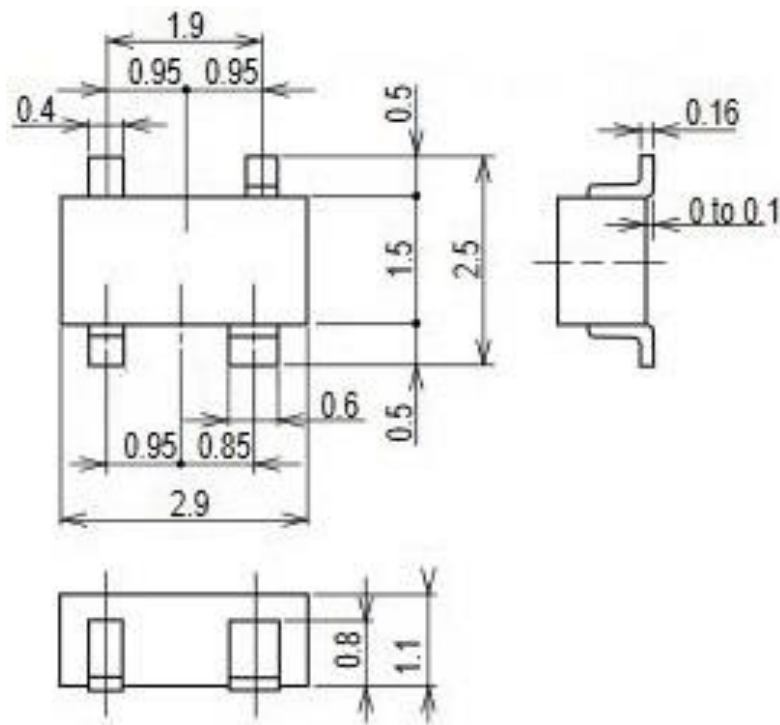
Габаритні розміри польового транзистора 3SK182
